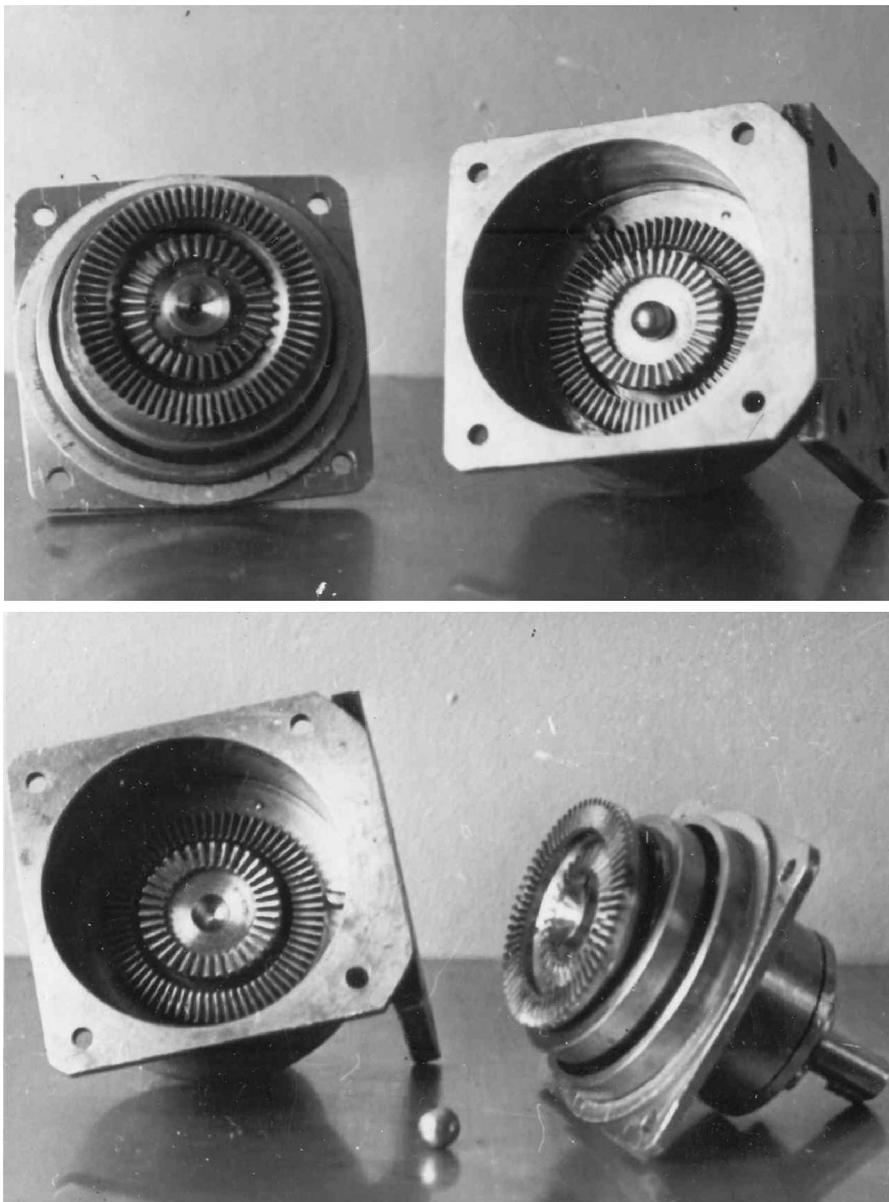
Редуктор конический торцевой планетарный (по рис. 1), конструктивные элементы редуктора в реальном исполнении
